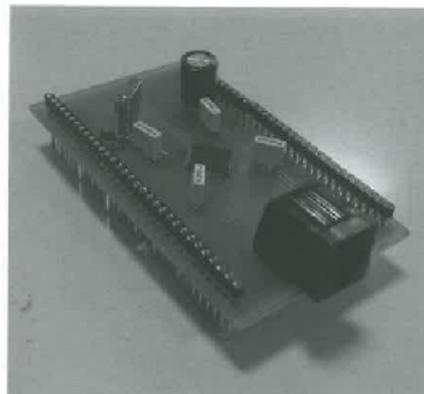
Soudage du microcontrôleur, carte de test.
